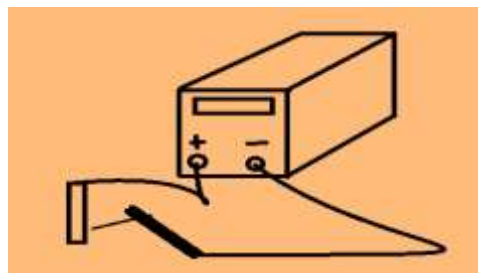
แสดงเครื่องเชื่อมแบบอินเวอร์เตอร์ (Inverter Welding)
